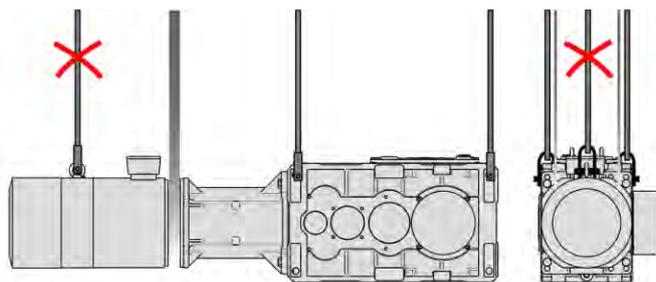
POSIRED 2 con flangia attacco motore e motore
